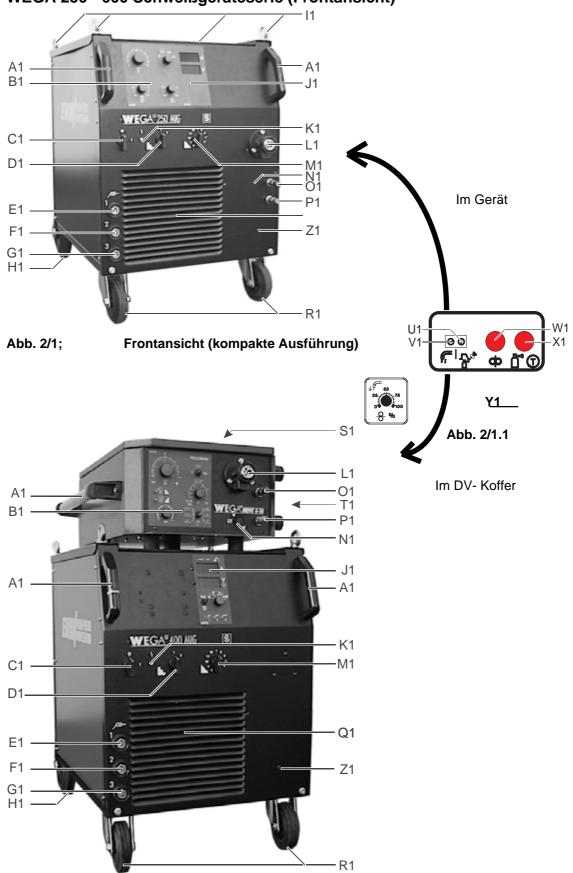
/2; Frontansicht (dekompakte Ausführung)
